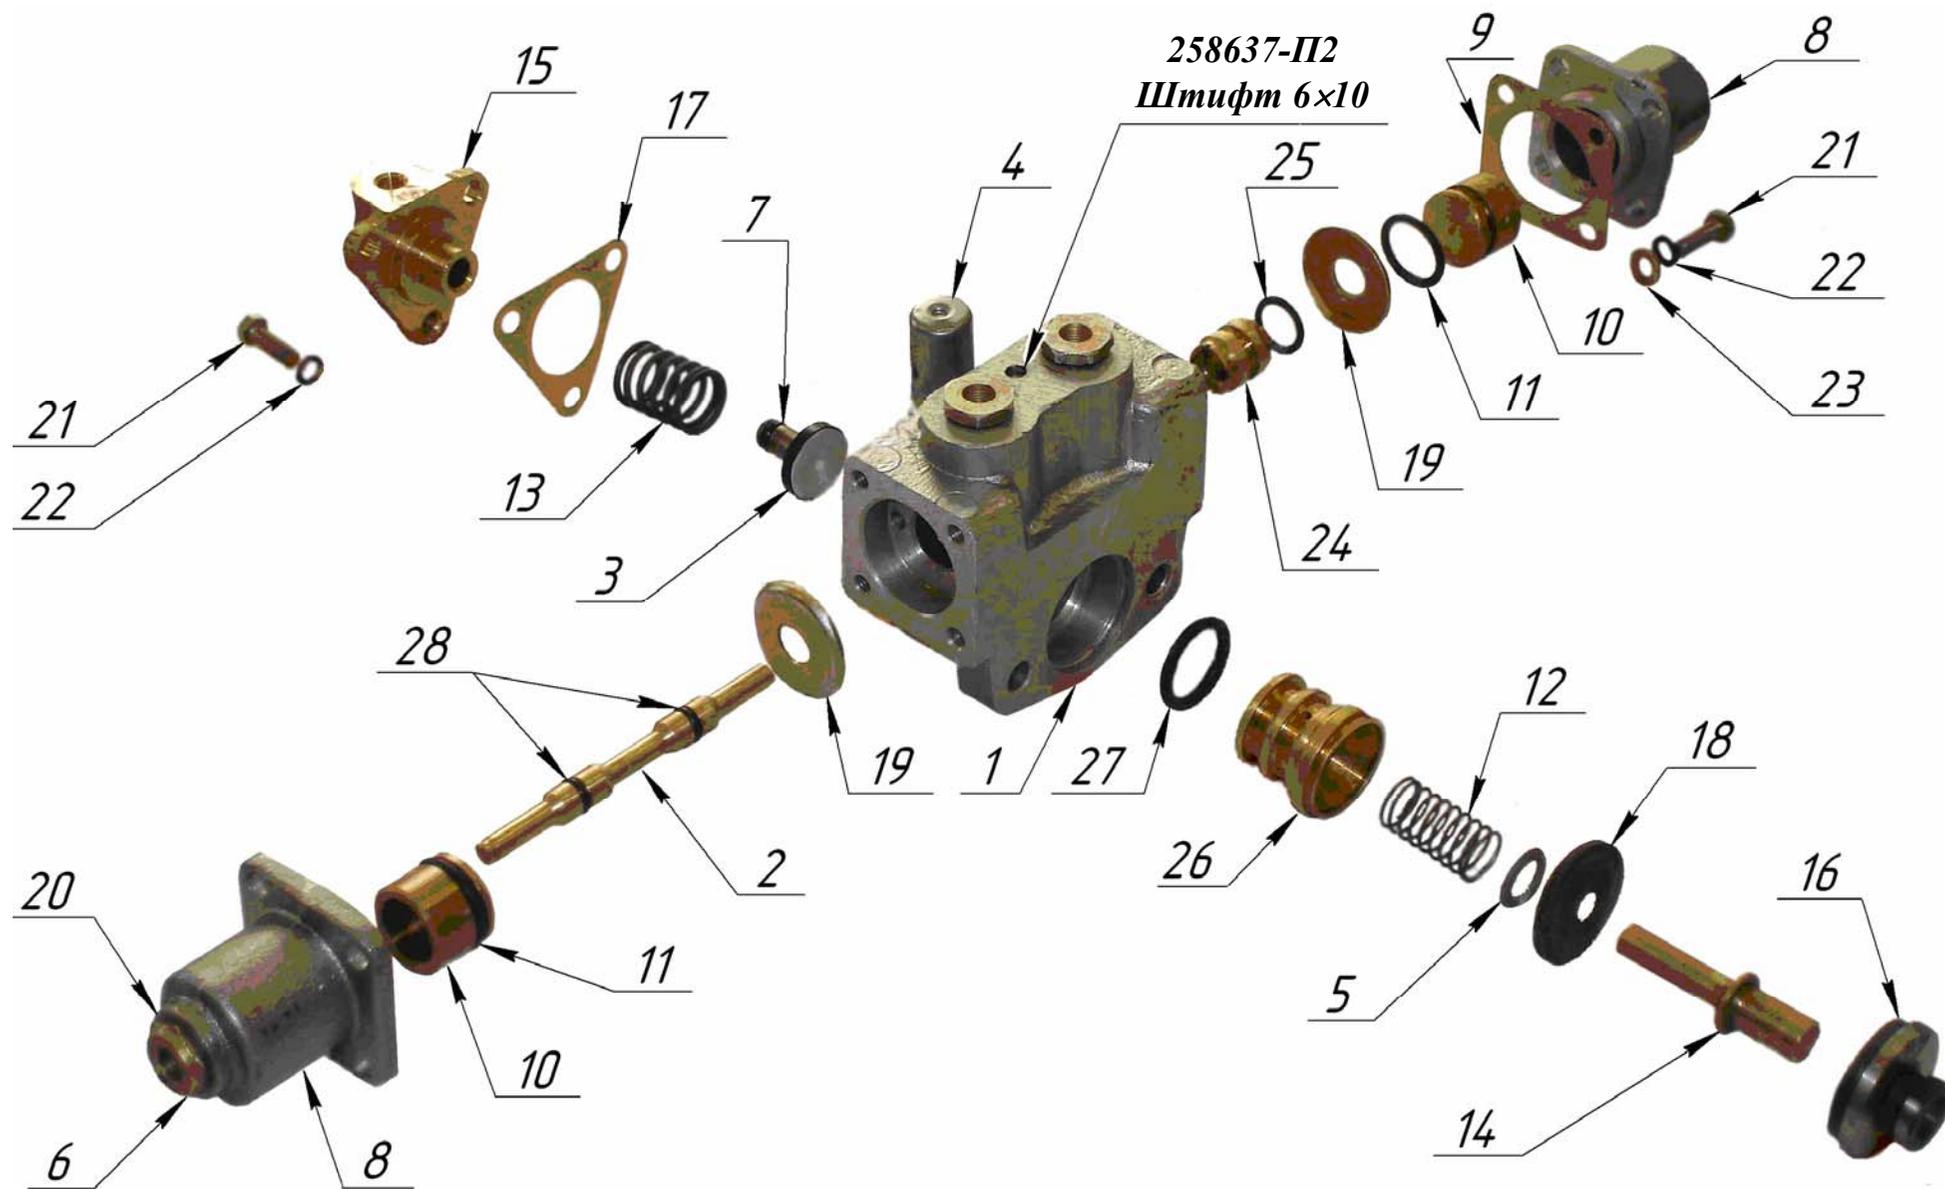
Внешний вид деталей разобранного воздухораспределителя КП ЯМЗ-239
